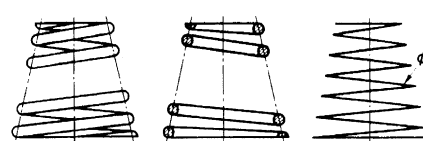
Kegelige Schraubendruckfeder aus Draht mit rundem Querschnitt
